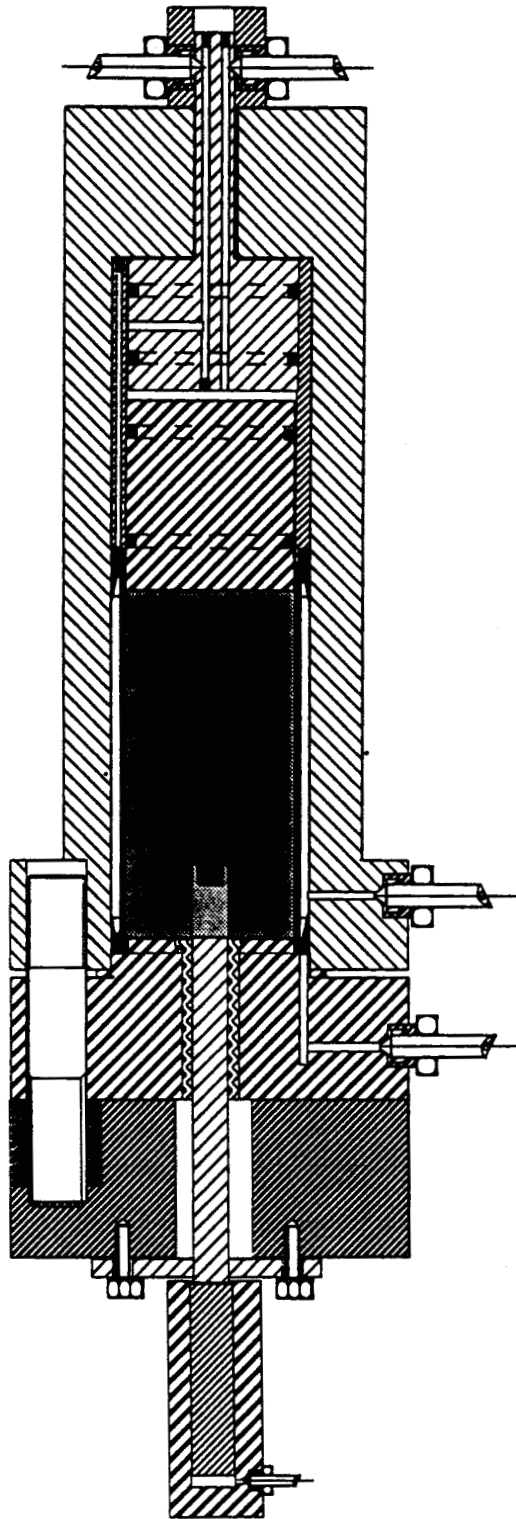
Schéma de la machine à disquer sous pression de boue
